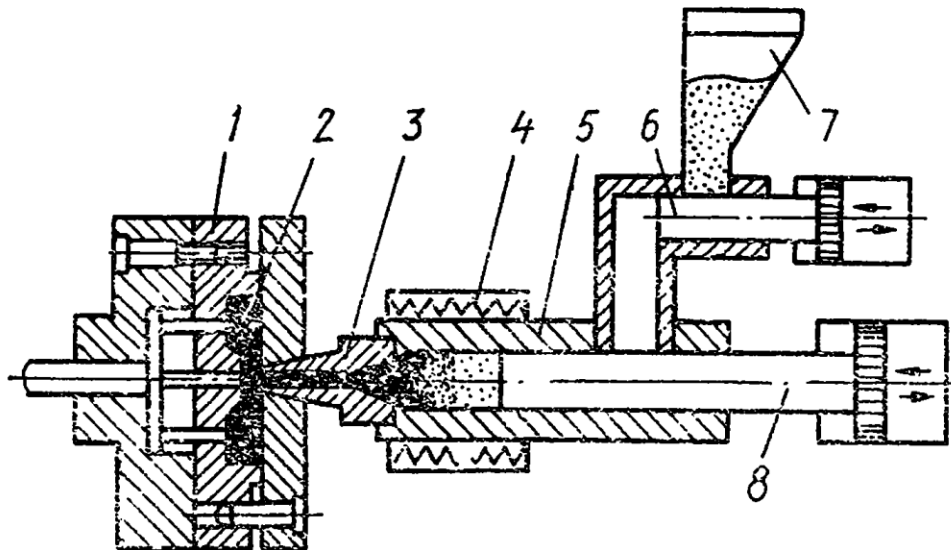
Схема дозуючого та пресувального пристроїв машин для лиття під тиском: 1 – прес-форма; 2 – виріб; 3 – сопло; 4 – електронагрівальний пристрій; 5 – ливарний циліндр; 6 – дозуючий плунжер; 7 – бункер; 8 – плунжер ливарного циліндра
